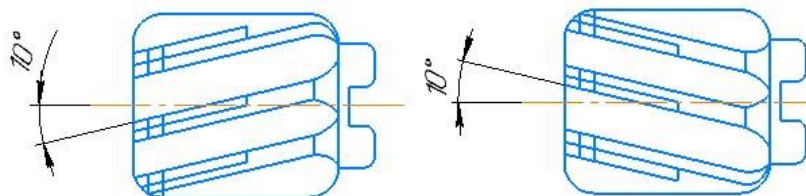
Насадна розвертка з гвинтовими твердосплавними пластинами
